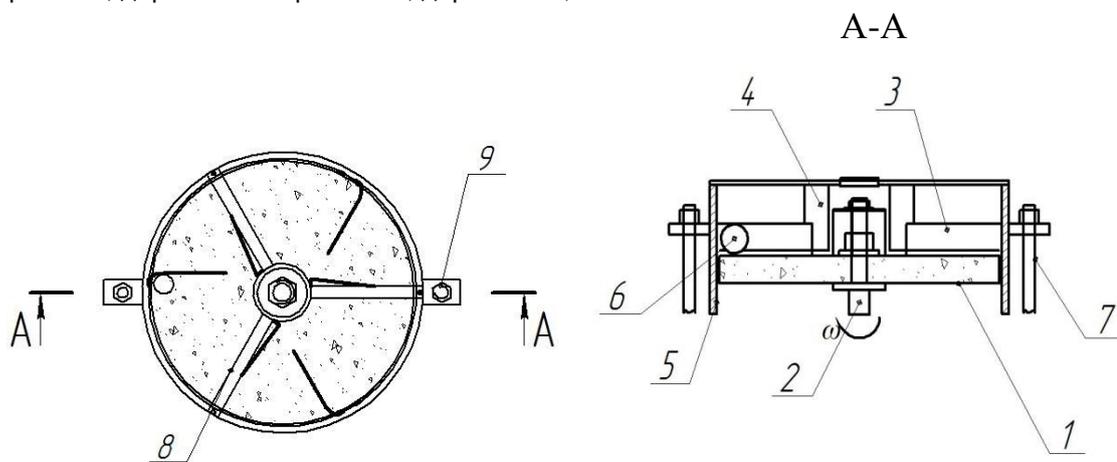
Устройство для обработки шариков из самоцветных камней
